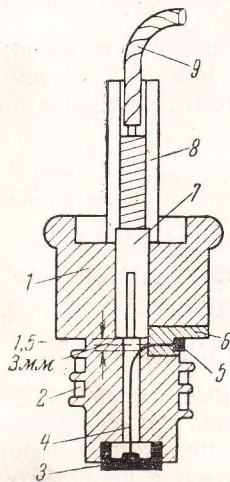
Пробочный предохранитель. 1 — корпус пробки; 2 — контактная резьба; 3 — контактный колпачок; 4 — плавкая вставка; 5 — пайка; 6 — замазка из мела с жидким стеклом; 7 — вилка диаметром 5 мм; 8 — фибровая трубка (изоляция) диаметр наружный 10 мм; 9 — провод;
